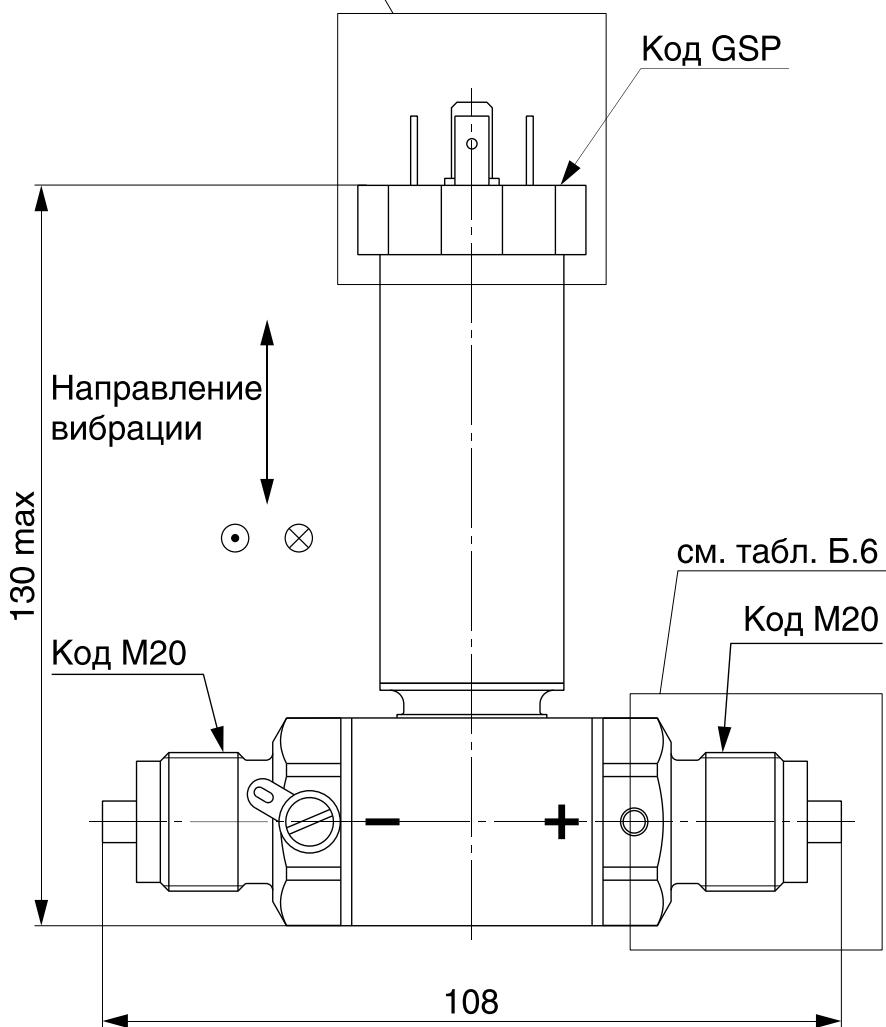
Габаритные и присоединительные размеры датчика
